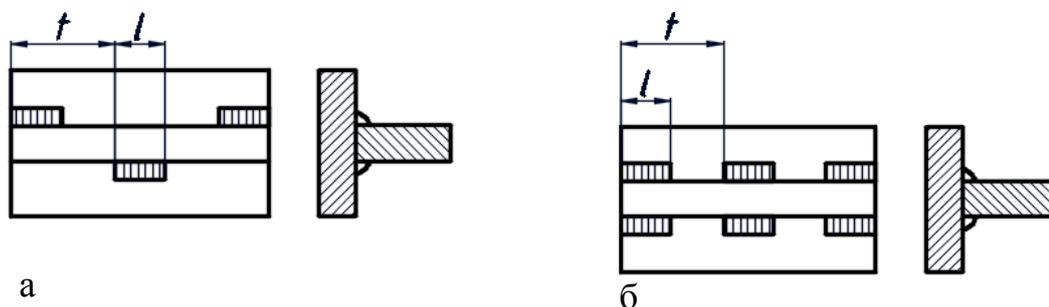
Образец выполнения сварных швов по протяженности.
